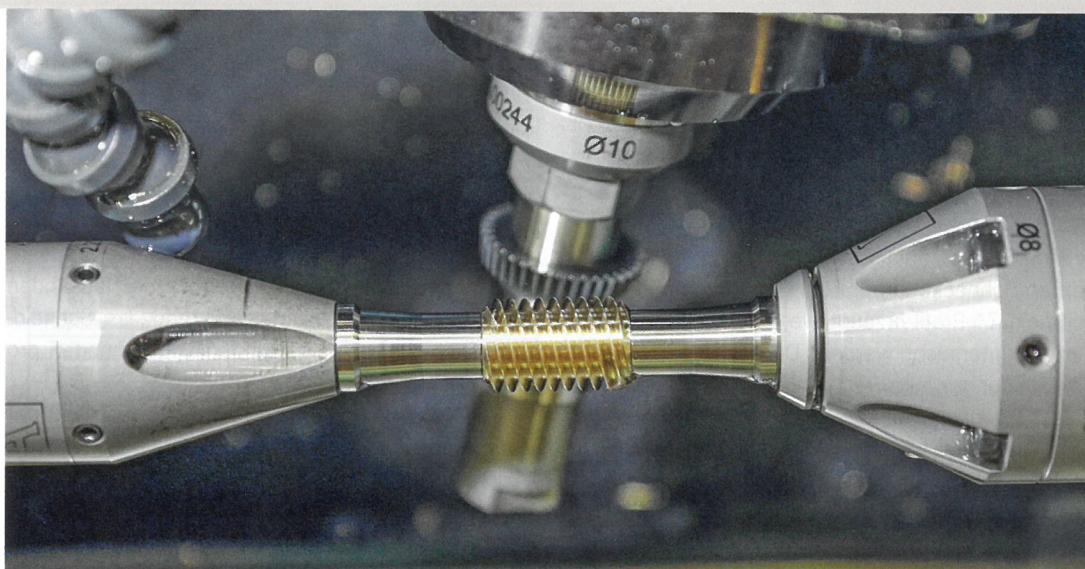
Anordnung des Schneidwerkzeugs zum Wälzschälen
